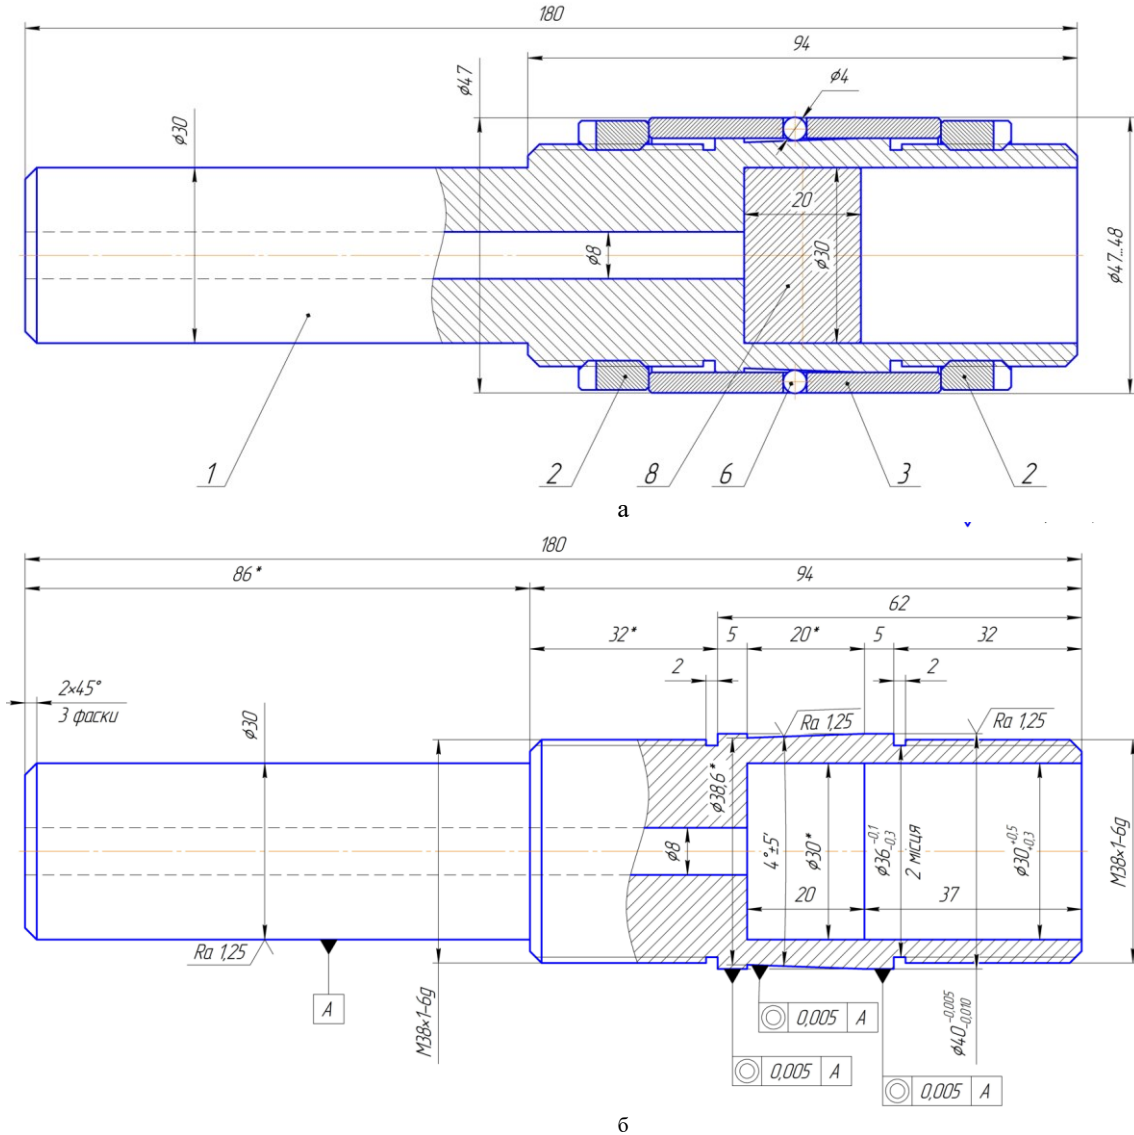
Інструмент для формування регулярного мікрорельєфу на внутрішній поверхні шатунних вкладишів:
